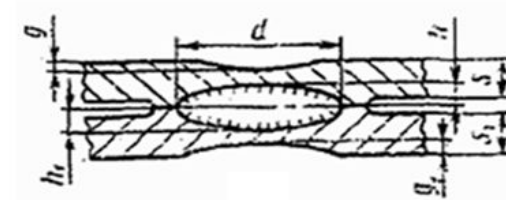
Конструктивные элементы соединения при контактной точечной сварке:
